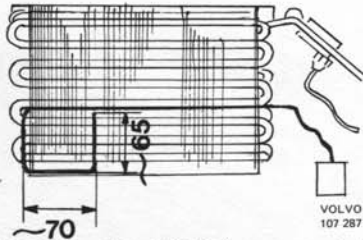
Einschub des Fühlkörpers zwischen den Kühlrippen des Kältemittelverdampfers spät. Ausf.
